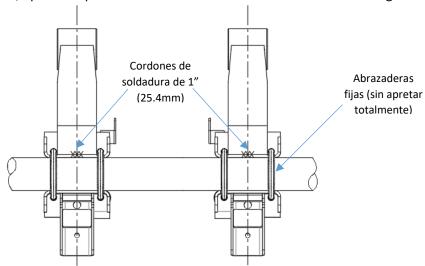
Ubicación de puntos previos de soldadura (vista inferior)
